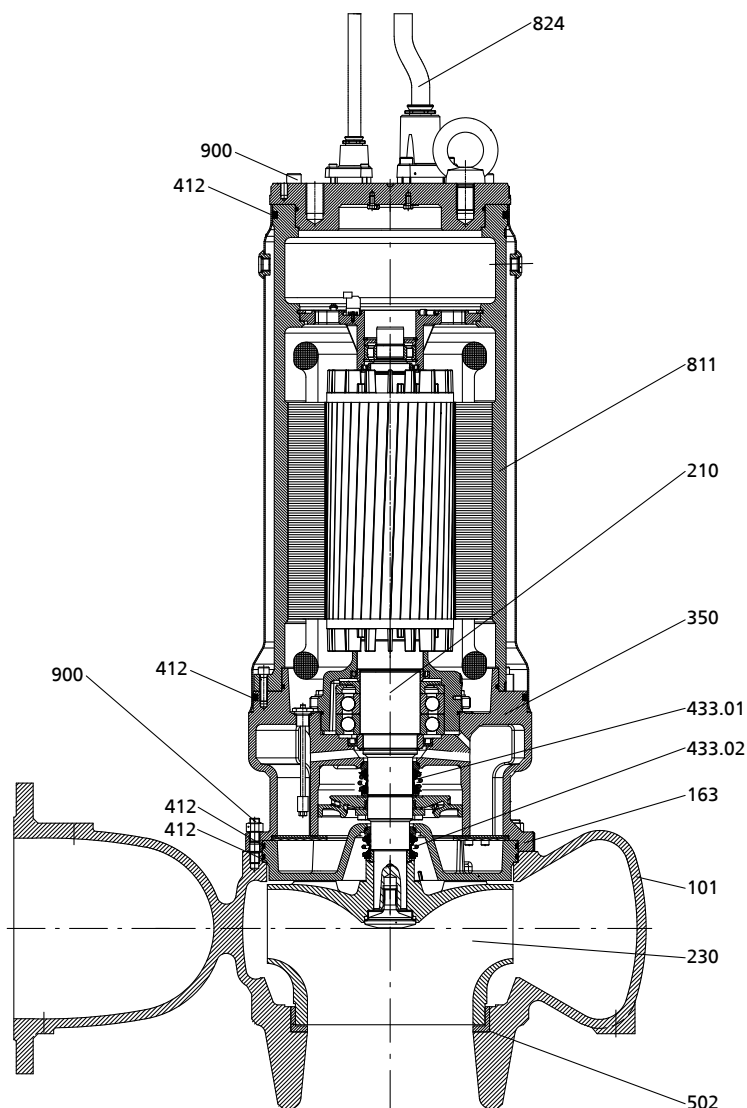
Сборочный чертеж, пример: KRT K 150-401 / 130 4 XNG-K с рубашкой охлаждения
